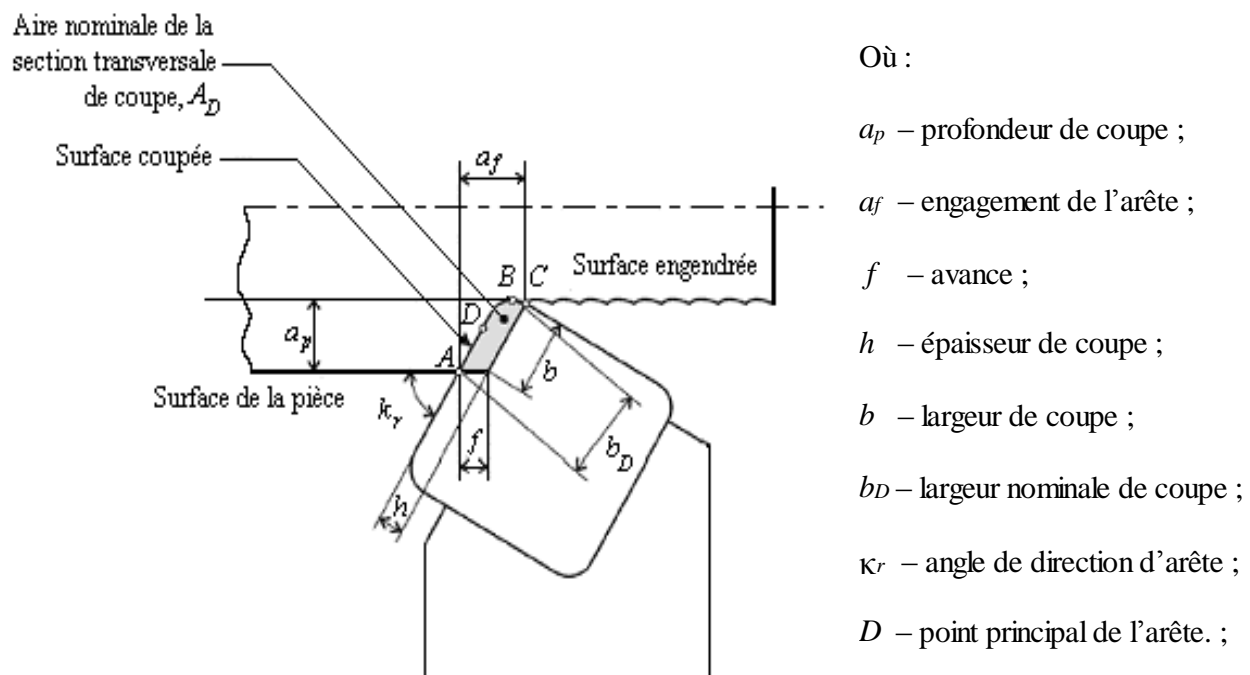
[23] : Dimensions de coupe dans le cas de tournage.
